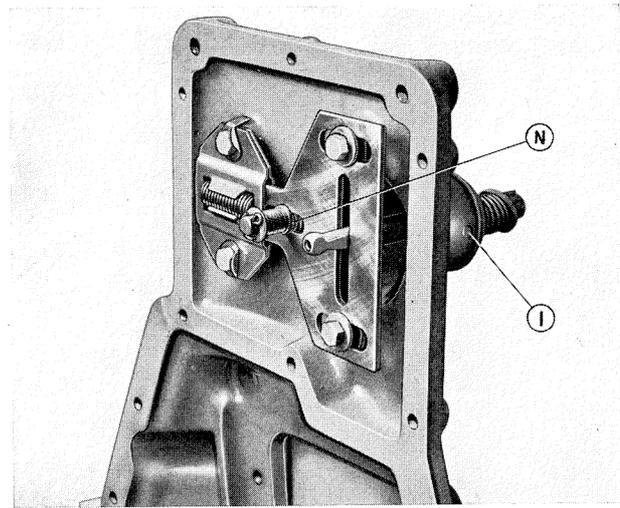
Vue par le dessous du couvercle de la boîte de vitesses.
